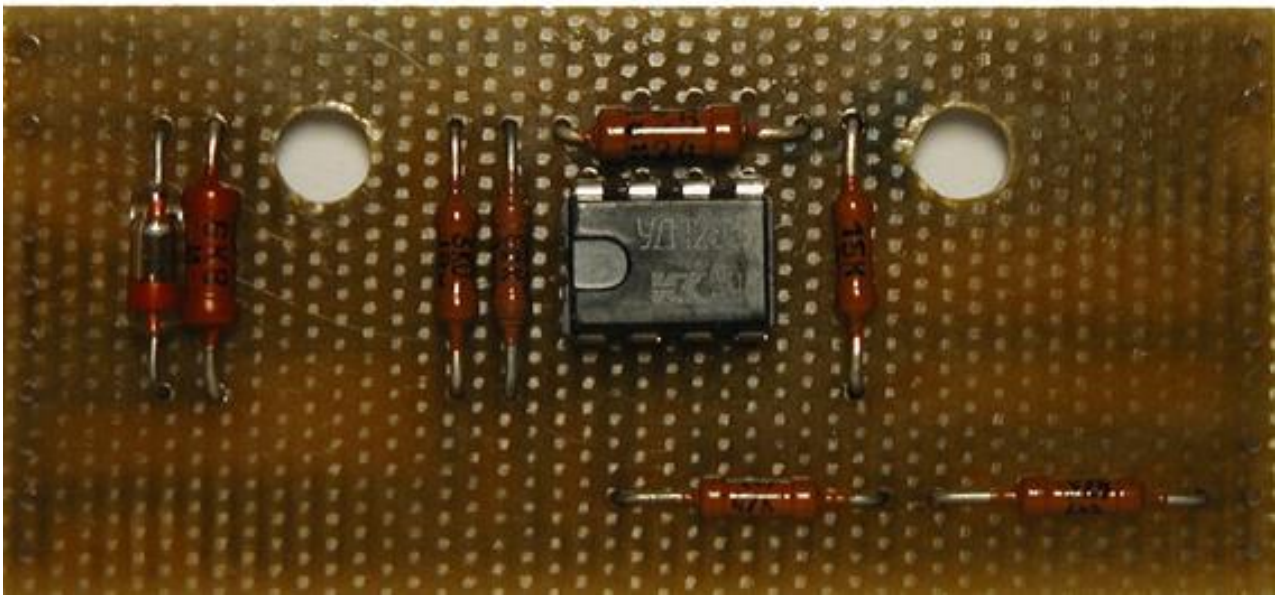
Плата для зборки основної схеми й схеми з корекцією шкали
